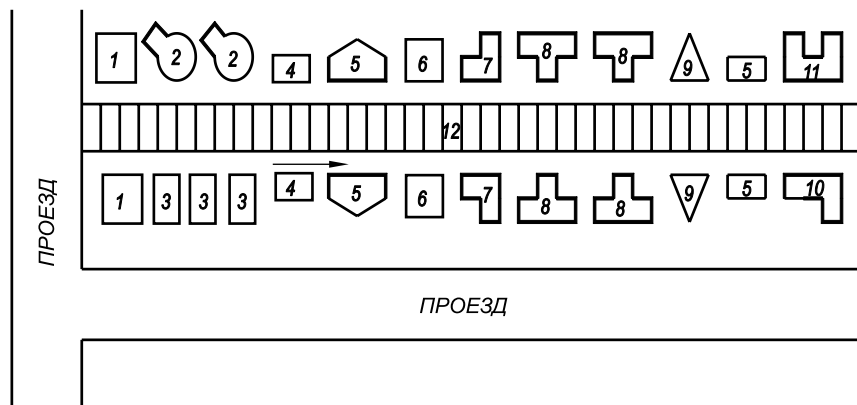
Схема поточной линии для обработки подшипниковых колец: 1 — тара для заготовок; 2 — токарные станки для обработки внутренних колец; 3 — токарные станки для обработки наружных колец; 4 — технический контроль; 5 — термическая печь; 6 — плоскошлифовальный станок; 7 — бесцентрово-шлифовальный станок; 8 — внутршлифовальный станок; 9 — доводочный станок; 10 — сборка подшипников; 11 — установка; 12 — транспортёр
